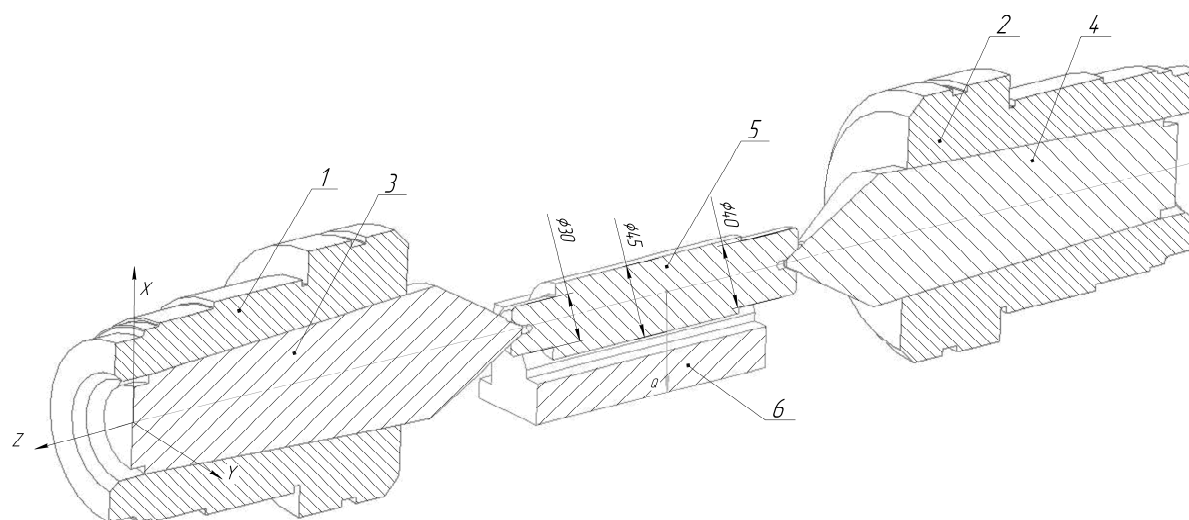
Конструкція двохповодкового двобічного фрикційного приводу деталі:
